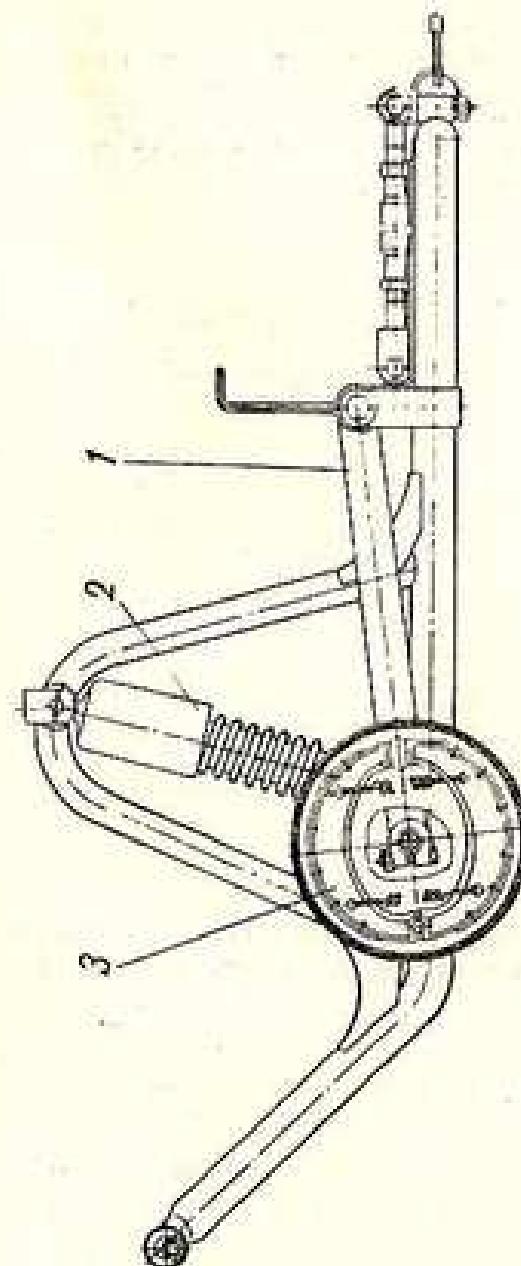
РАМА БОКОВОГО ПРИЦЕПА
